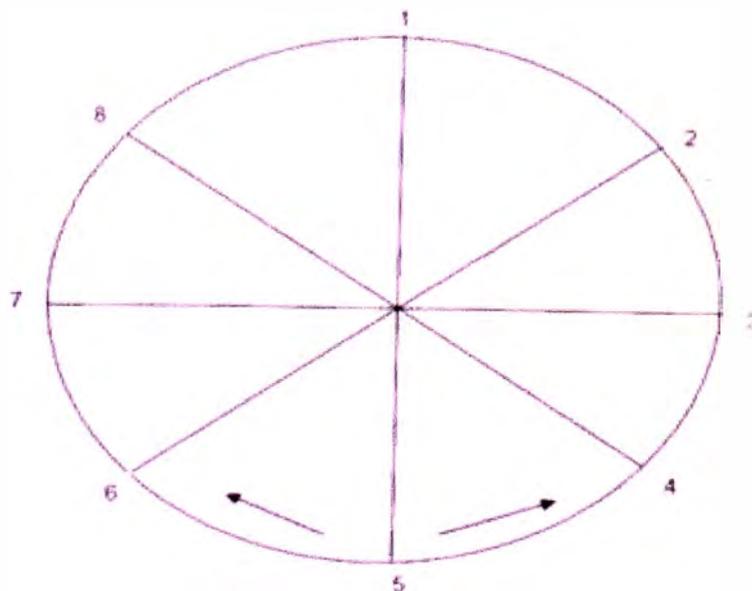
Posiciones y tramos a soldar (Vista de soldeo entre tramos 5-6 y 5-4, alternada y opuesta a la figura 5.18)
